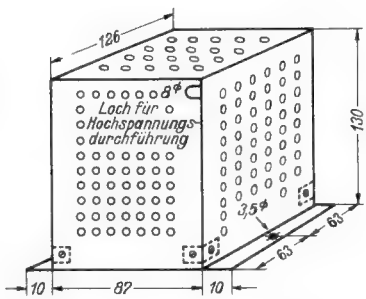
Abschirmhaube. Aluminium 1 mm, halbhart; Luftlöcher 7 mm Ø; Ecke unter dem Loch für die Hochspannungsdurchführung nach dem Einschieben des Kabels verschrauben.
